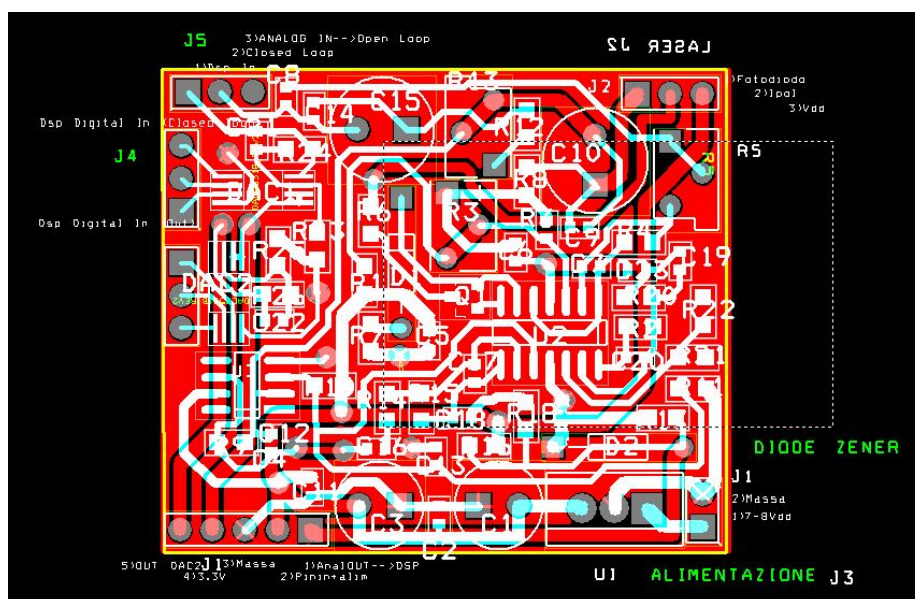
Realizzazione del PCB tramite ORCAD Layout di Cadence.
